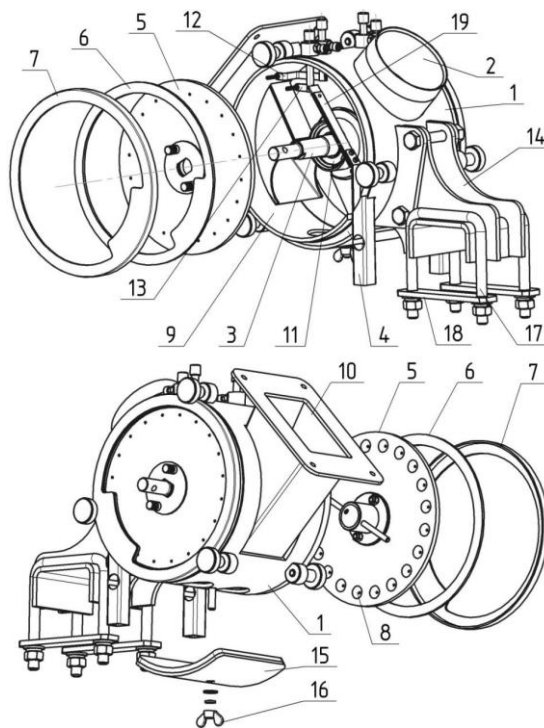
Схема експериментального висівного апарату: 1 – корпус; 2 – патрубок; 3 – вал; 4 – забірний пристрій; 5 – висівний диск; 6 – прокладка; 7 – кришка; 8 – дозуючий елемент; 9 – нагнітальна камера; 10 – горловина; 11 – корпус підшипника; 12 і 13 – скидачі; 14 – кронштейн; 15 – люк вивантажний; 16 – гайка; 17 – хомут; 18 – планка; 19 – захисний екран [22].
